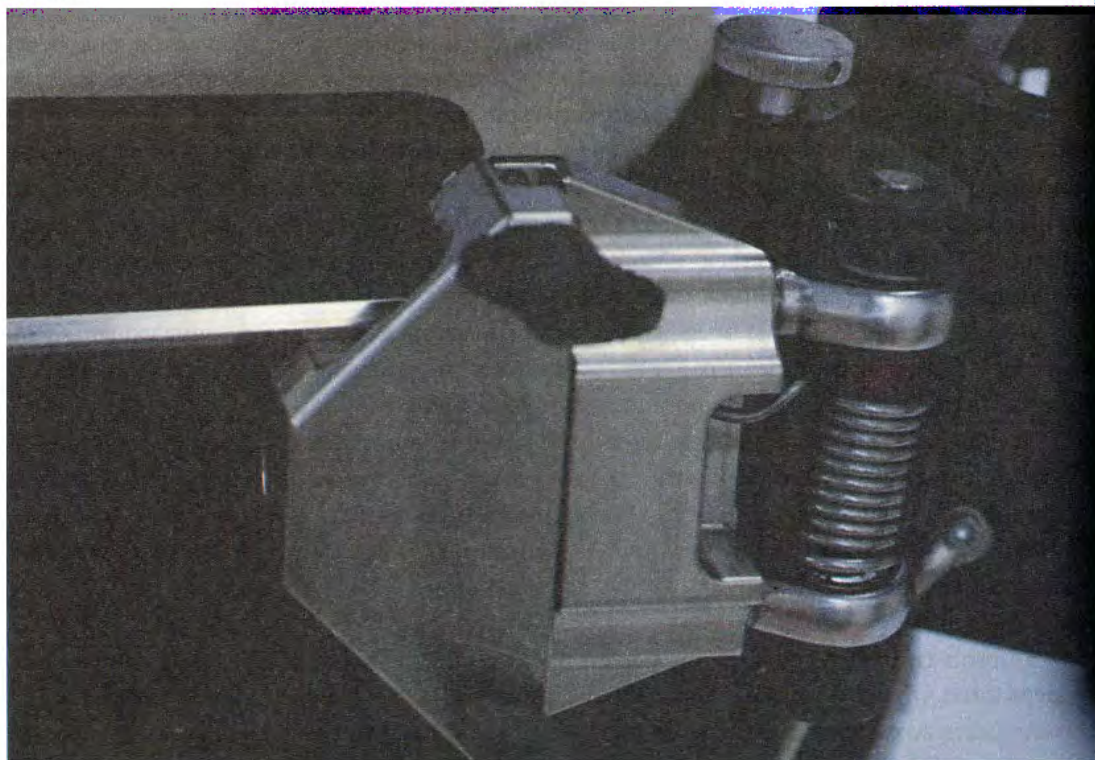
с. Регулируем наклон руки-амортизатора «вправо-влево». Типичное положение верхнего и нижнего подшипников со стержневым концом.
